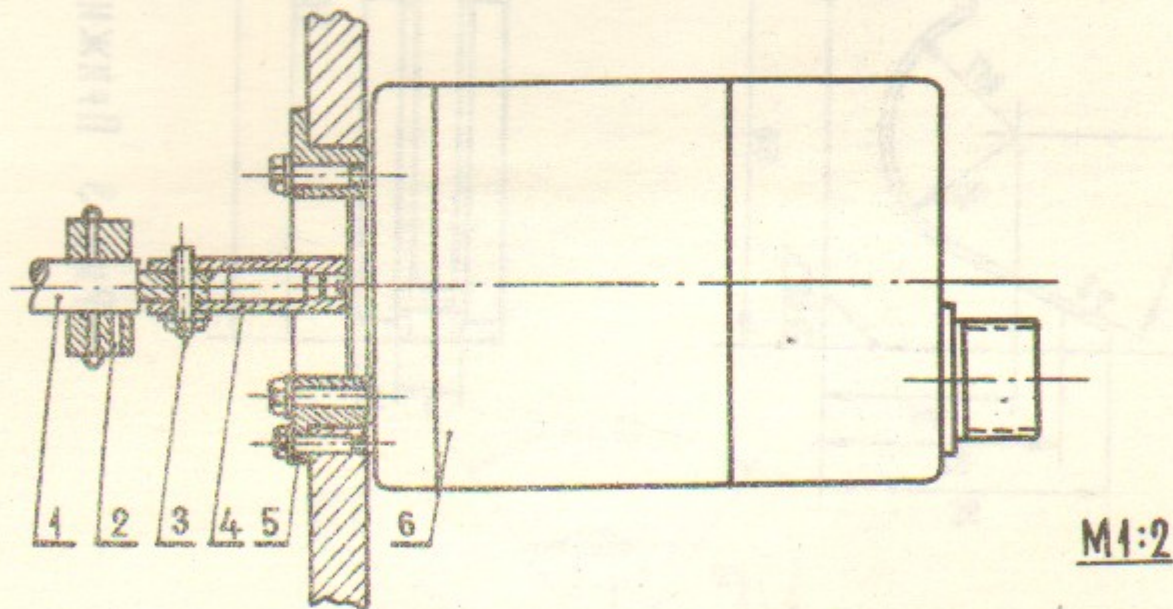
Установка ШД-4 вместо электромагнитной муфты нового образца
